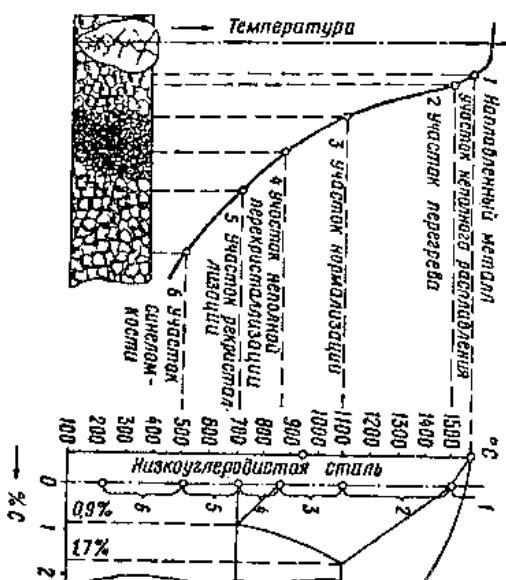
Строение зоны термического влияния сварного шва
